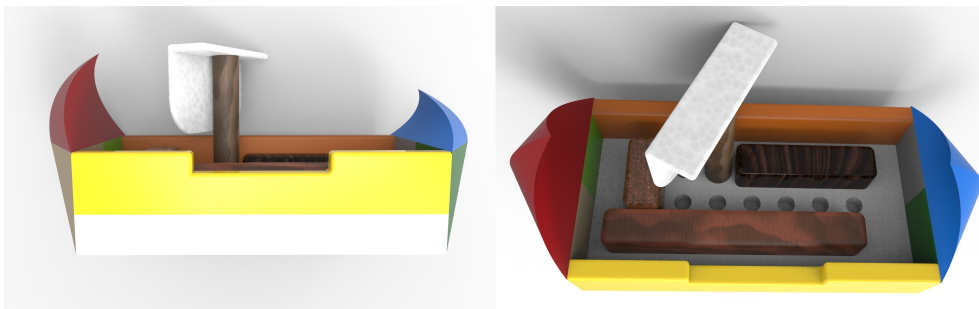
Fotorrealismos do primeiro CAD tridimensional das peças assembledas.
